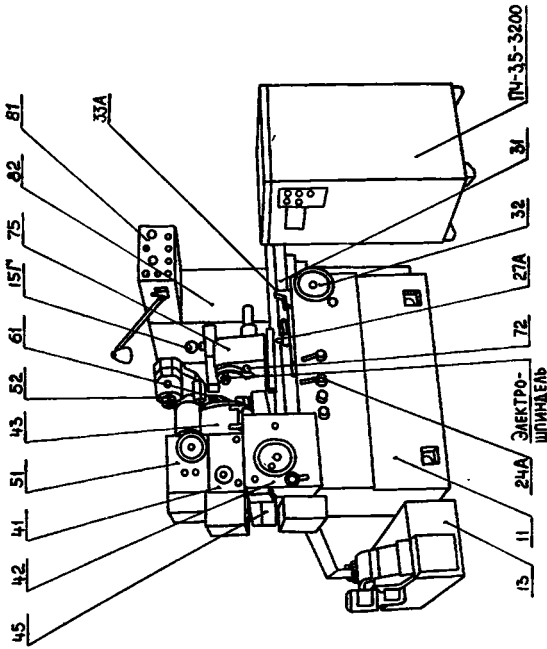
Общий вид станка модели 3К225А с обозначением узлов
